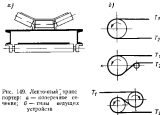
Ленточный транспортер: а — поперечное сечение; б — типы вращающихся устройств
